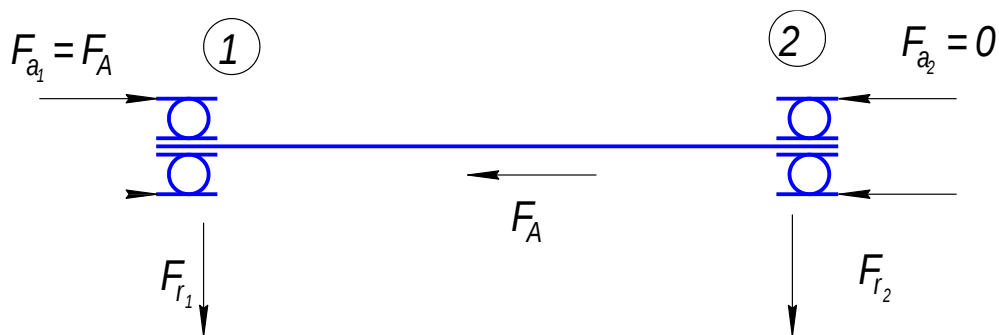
Схема действия нагрузок на подшипники ведущего вала
